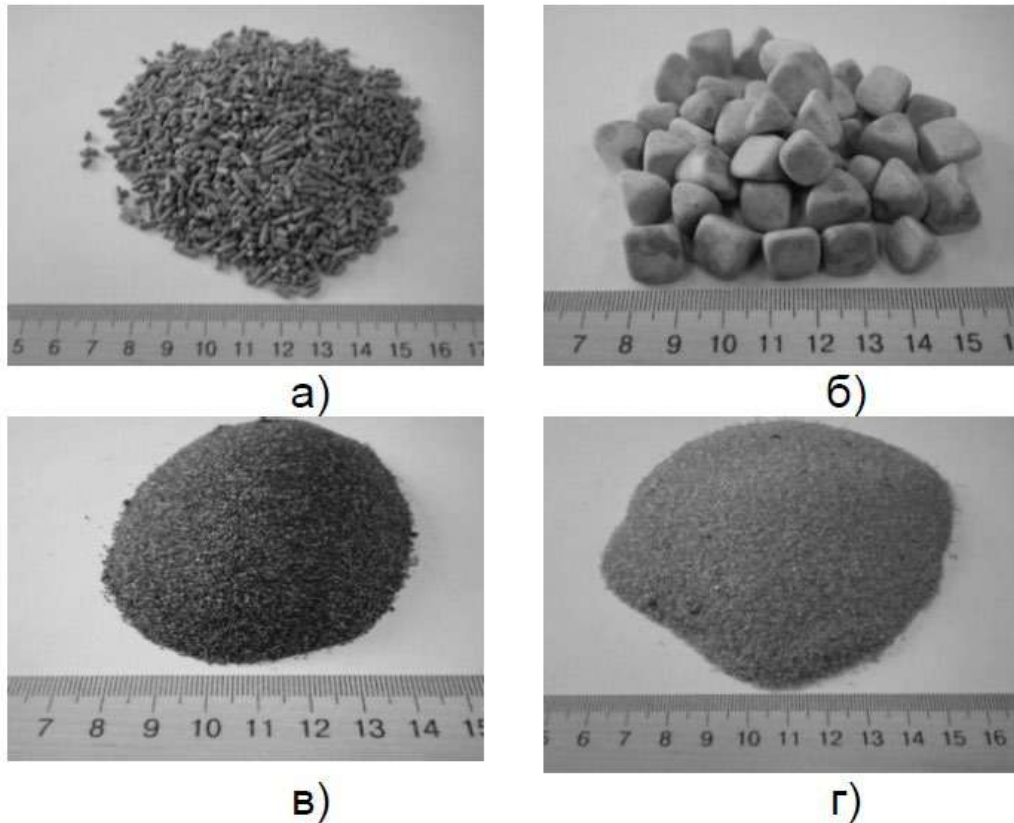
Робочі середовища для обробки: а - формокорунд - циліндр \emptyset 2x5...8 мм; б) - ПТ-10; в) - шліфзерно; г) - волзький пісок
